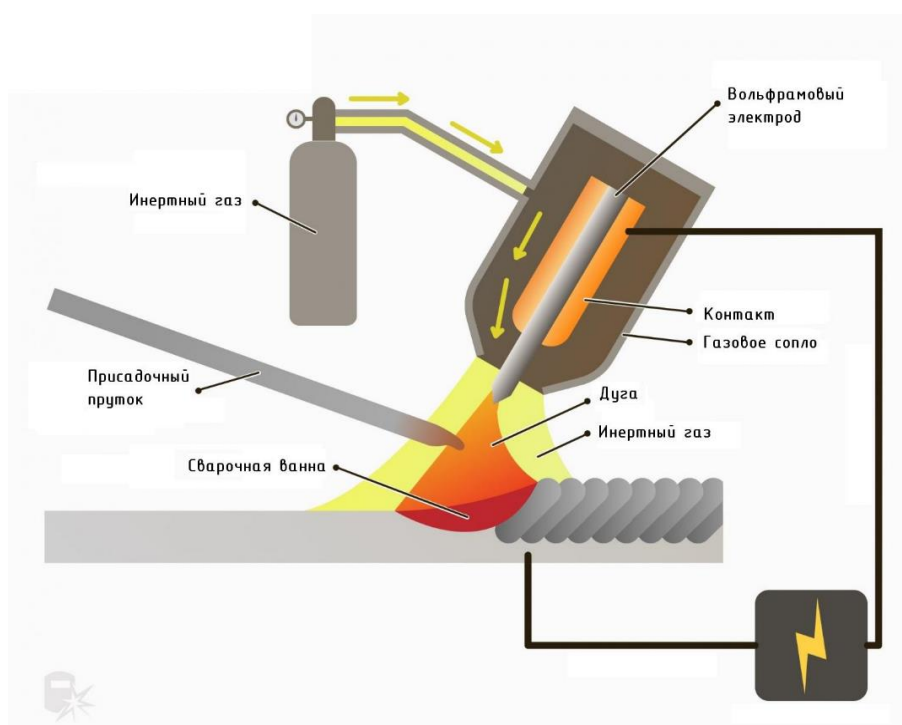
Схема сварки неплавящимся электродом
